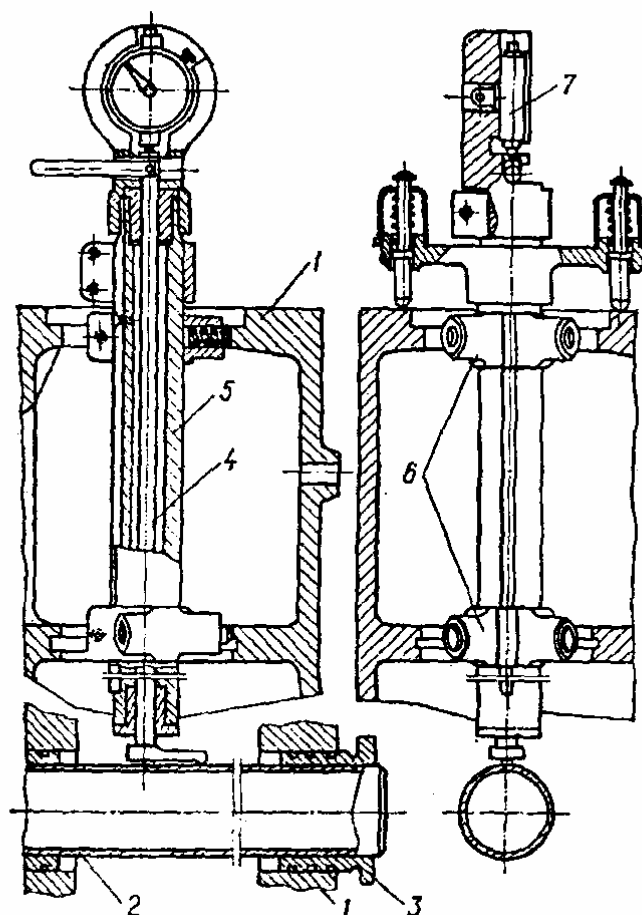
Схема перевірки перпендикулярності осей отворів блока під гільзи до привалкової площини блока і до загальної осі опор колінчастого вала: 1 – блок циліндрів; 2 – оправка; 3 – втулка (дві); 4 – плунжер; 5 – колонка; 6 – самовставні фіксатори; 7 – індикаторна головка
